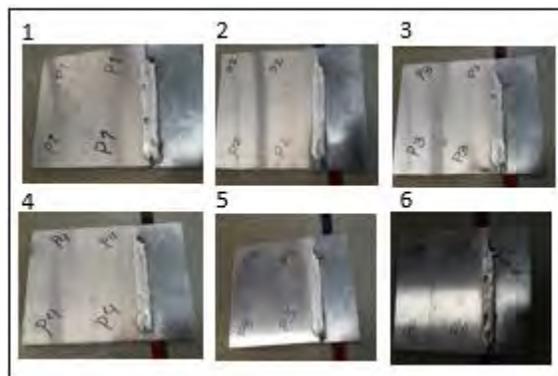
Cordones de soldadura del proceso CMT a un ángulo de 45°
